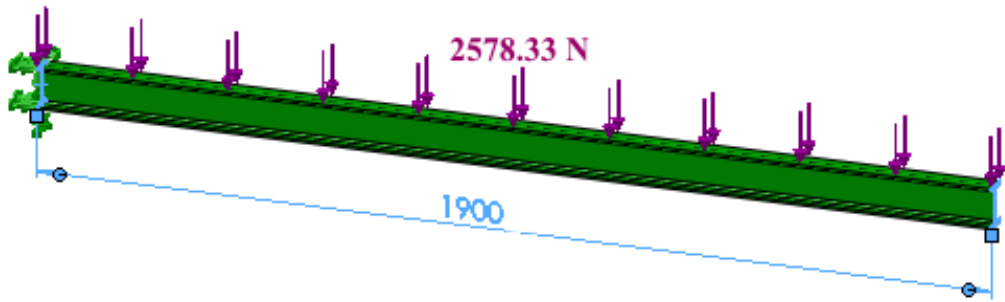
Diagrama de fuerzas de la viga de la estructura del plato giratorio.
